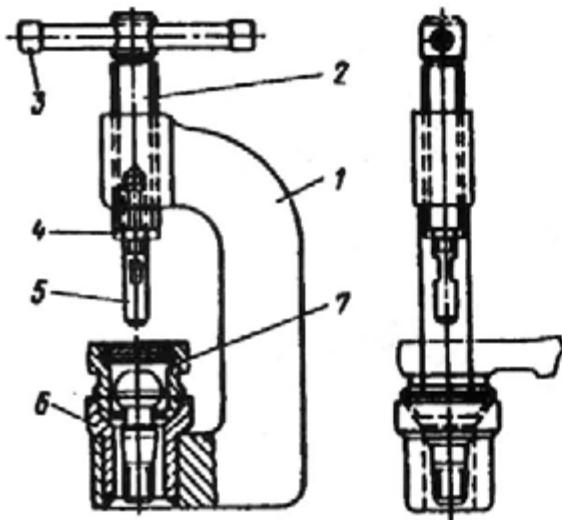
Приспособление для сборки шарниров рулевых тяг:
